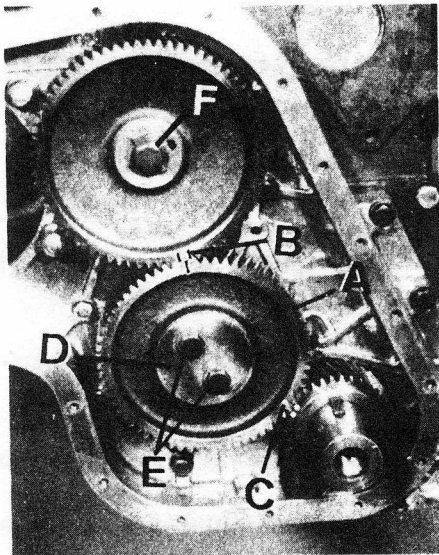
Montaje del engranaje de enlace (sincronizado de marcas)
